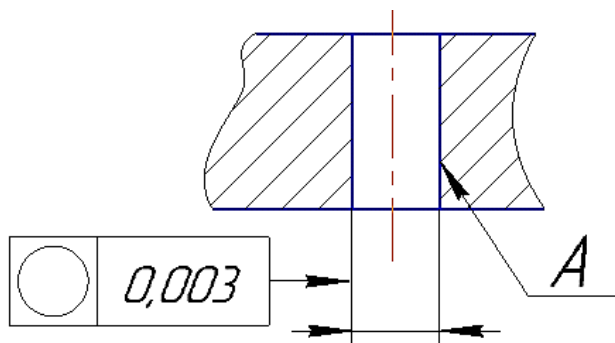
Указание на чертежах допусков формы цилиндрических деталей
